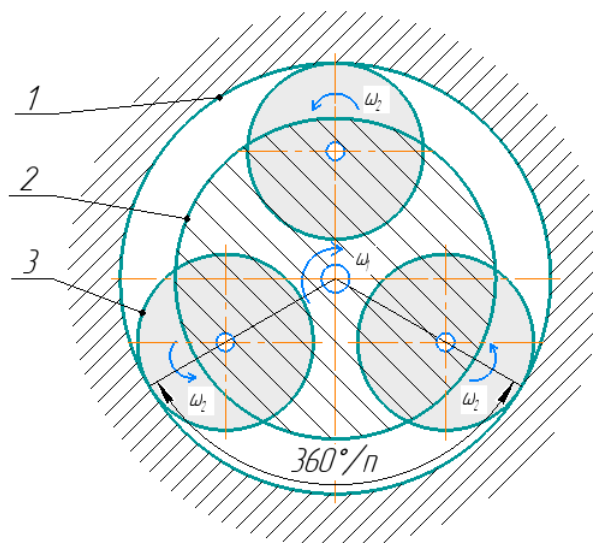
Кинематическая схема нового устройства для глубокого уплотнения грунтов на виде сверху:
